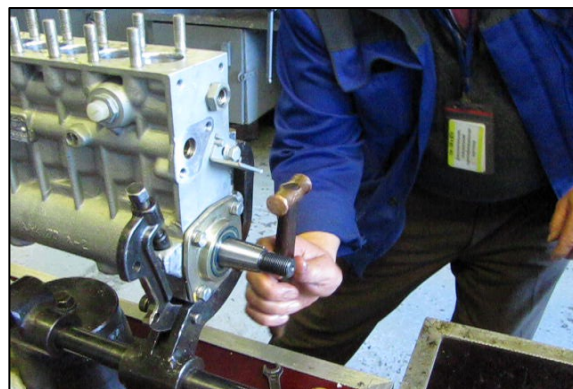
Запрессовка шпонки кулачкового вала
